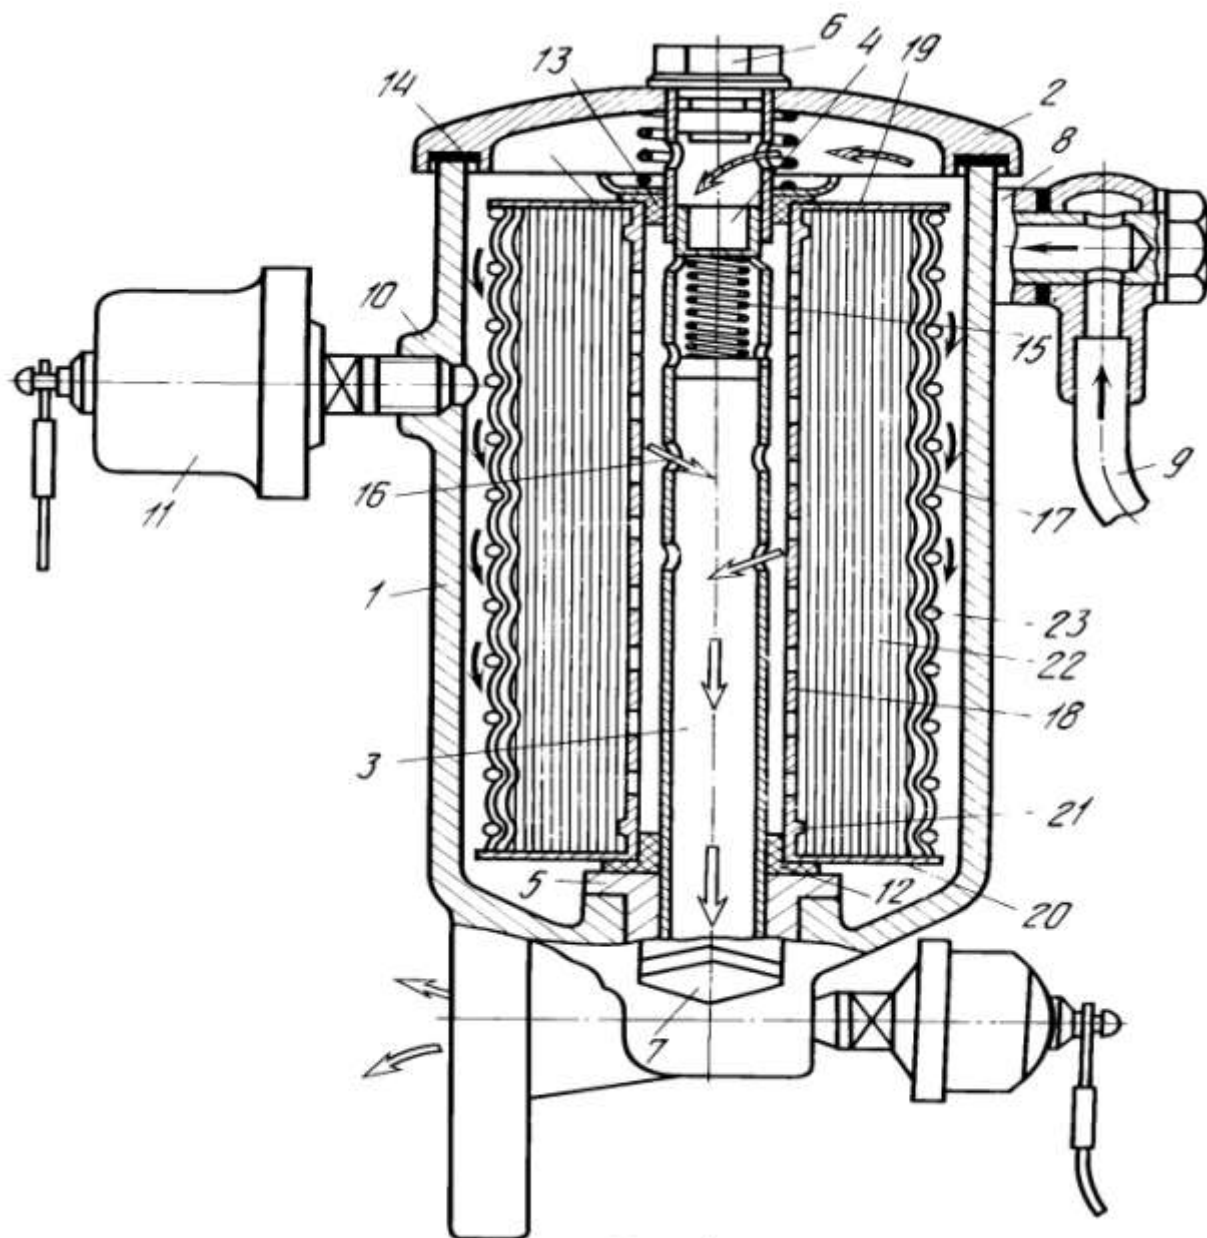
Масляный фильтр автомобиля ГАЗ-24 «Волга»: 1 – корпус; 2 – крышка; 3 – центральный стержень; 4 – перепускной клапан; 5 – резьбовое отверстие втулки; 6 – шестигранная головка; 7 – пробка; 8,10 – бобышки; 9 – трубка подвода масла к фильтру; 11 – датчик давления масла; 12,13,14 – резиновые прокладки; 15 – пружина; 16 – отверстия для прохода масла; 17 – фильтрующий элемент; 18 – перфорированный цилиндр; 19,20 – металлические донышки; 21 – маслозадерживающие кольца; 22 –
